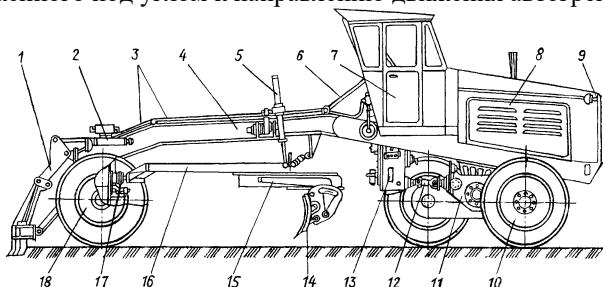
Конструктивная схема автогрейdera: 1 – рыхлитель; 2,5 – гидроцилиндры; 3,12 – карданные валы; 4 – основная рама; 6 – вал рулевого колеса; 7 – кабина; 8 – двигатель; 9 – радиатор; 10 – задний мост; 11 – сцепление; 13 – коробка перемены передач; 14 – отвал; 15 – поворотный круг; 16 – тяговая рама; 17 – цапфа переднего моста; 18 – передний мост. [5]
